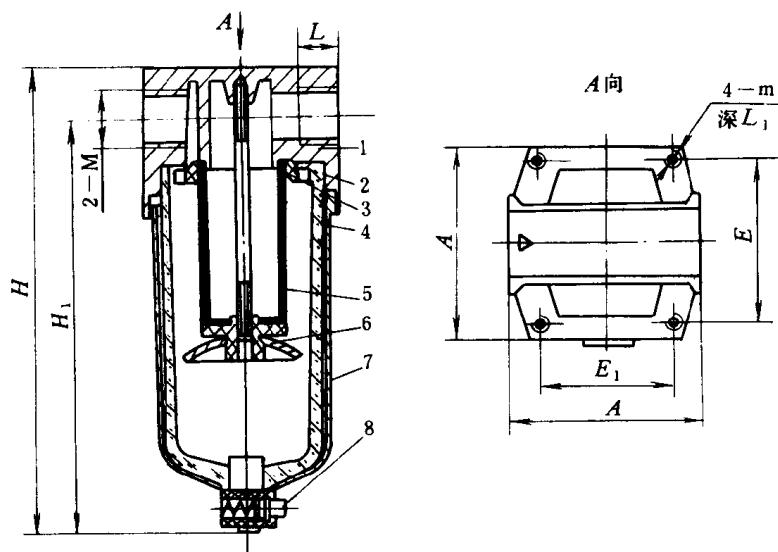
QSLB 系列空气过滤器结构原理及外形尺寸图
